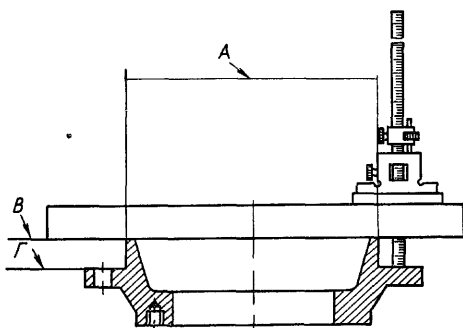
Проверка непараллельности поверхностей фланцевой крышки
